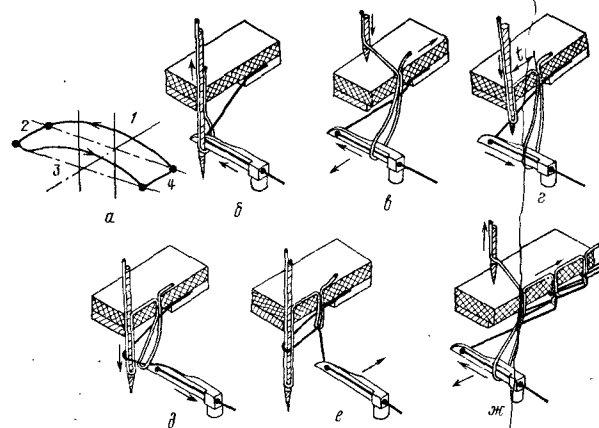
Процесс образования двухниточного цепного стежка петлителем с глазком
